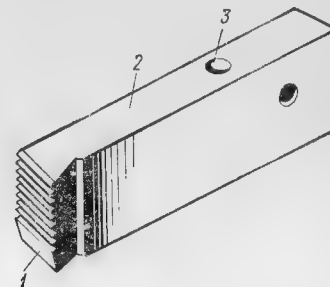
1 — рабочая часть; 2 — державка; 3 — отверстие
